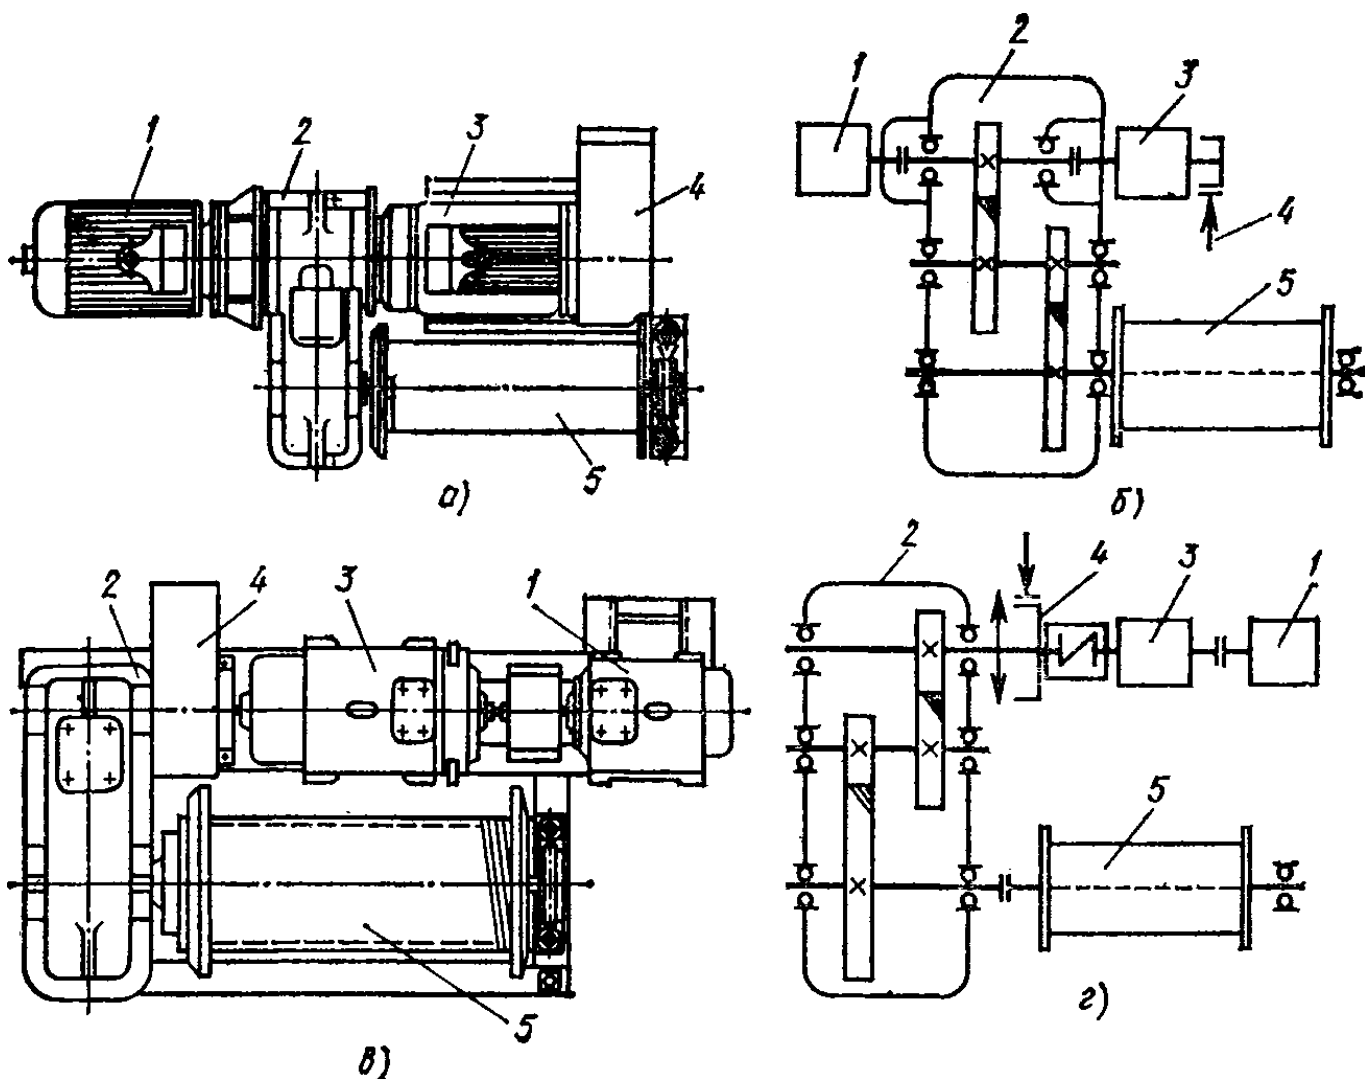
Двухдвигательные подъемные лебедки с размещением двигателей:
